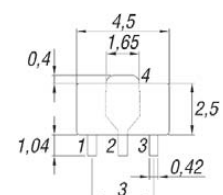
Pinbelegung (SOT-89) und Gehäuseabmessungen (nicht maßstäblich)
